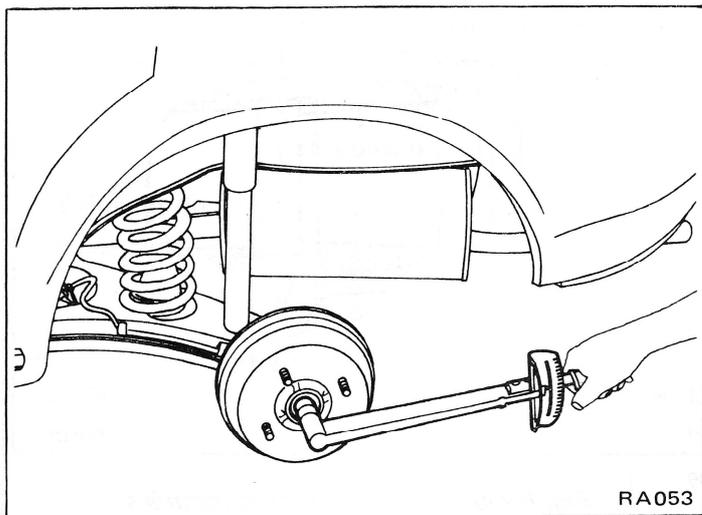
Serrage de l'écrou de blocage de roulement de roue
